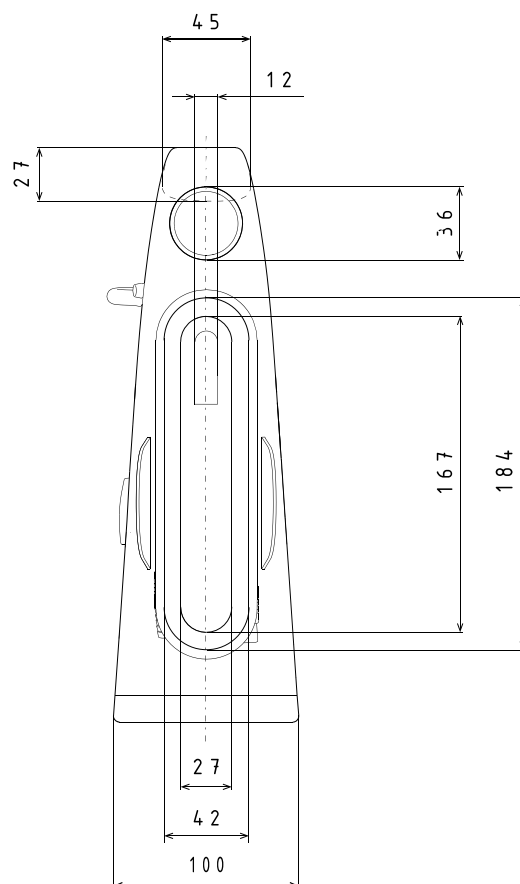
Základní rozměry (M 1:3): přední pohled.
